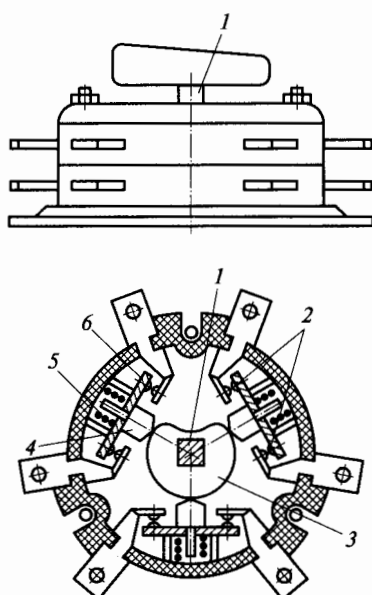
Пакетный кулачковый выключатель серии ПКВ:
